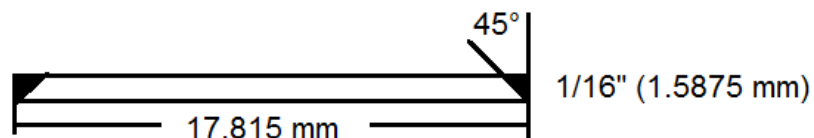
Sobre espesor de soldadura de 1/16".
